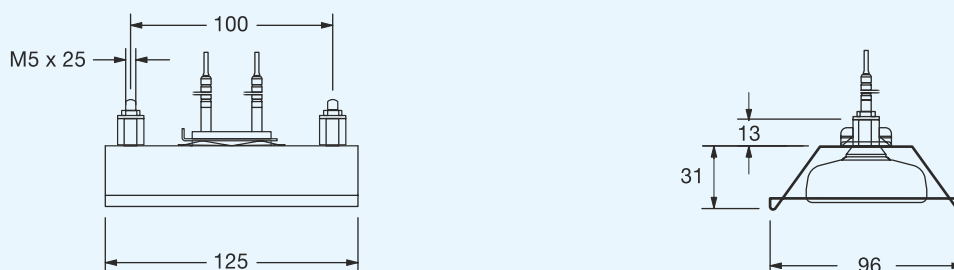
Монтажные размеры и габариты нагревателей () в мм
